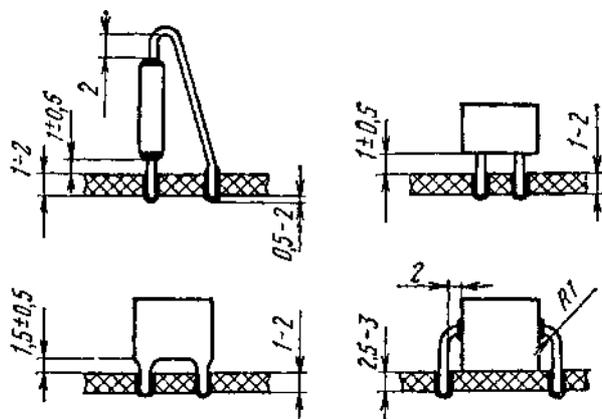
Вертикальная установка конденсаторов на печатных платах
